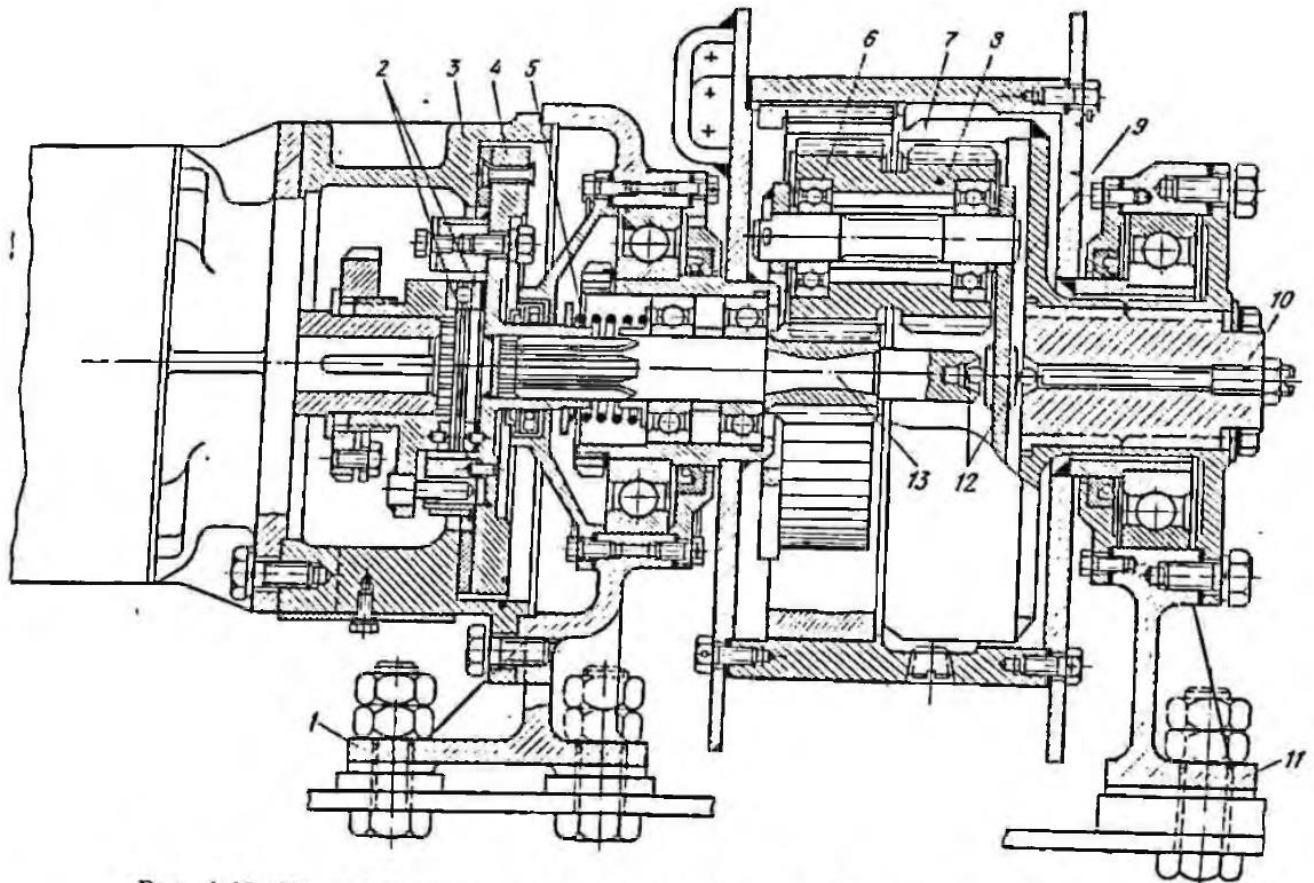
Механізм зміни вильоту стріли екскаватора Е-6516 [2, 5-7, 12]
